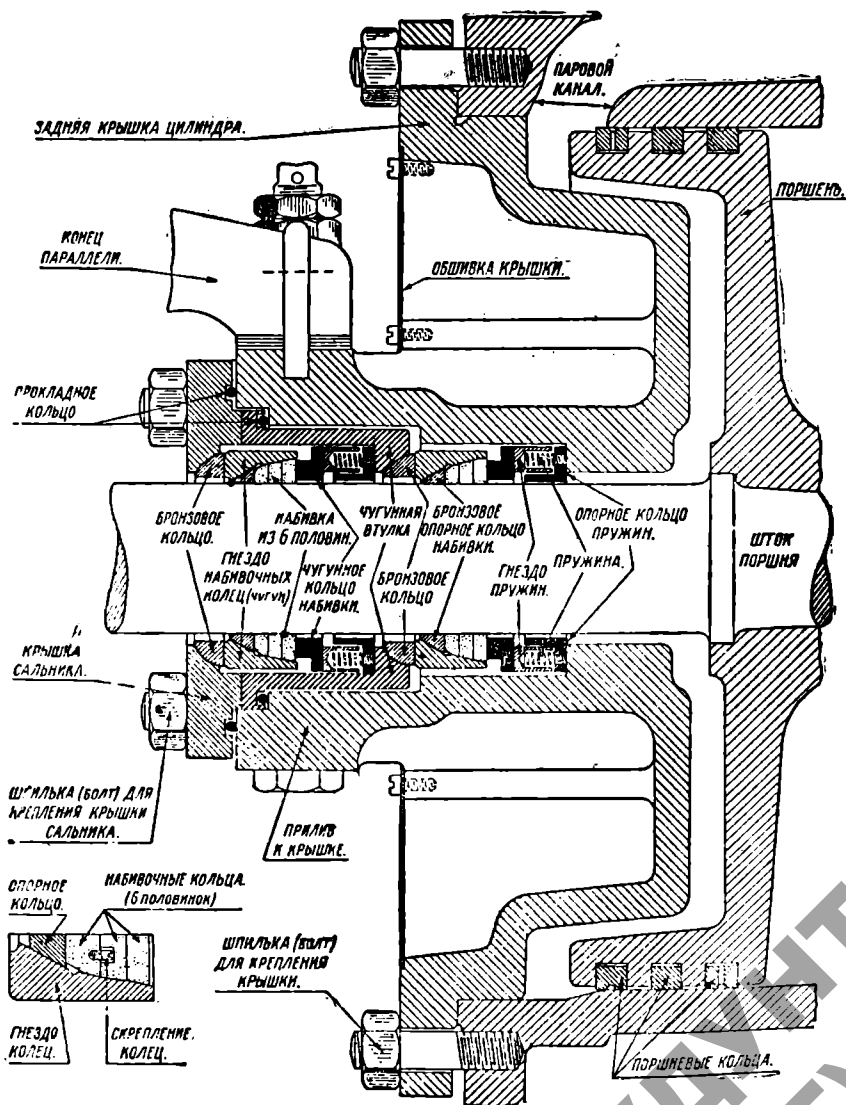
Сальник с металлической набивкой и задняя крышка цилиндра паровоза серии С.
